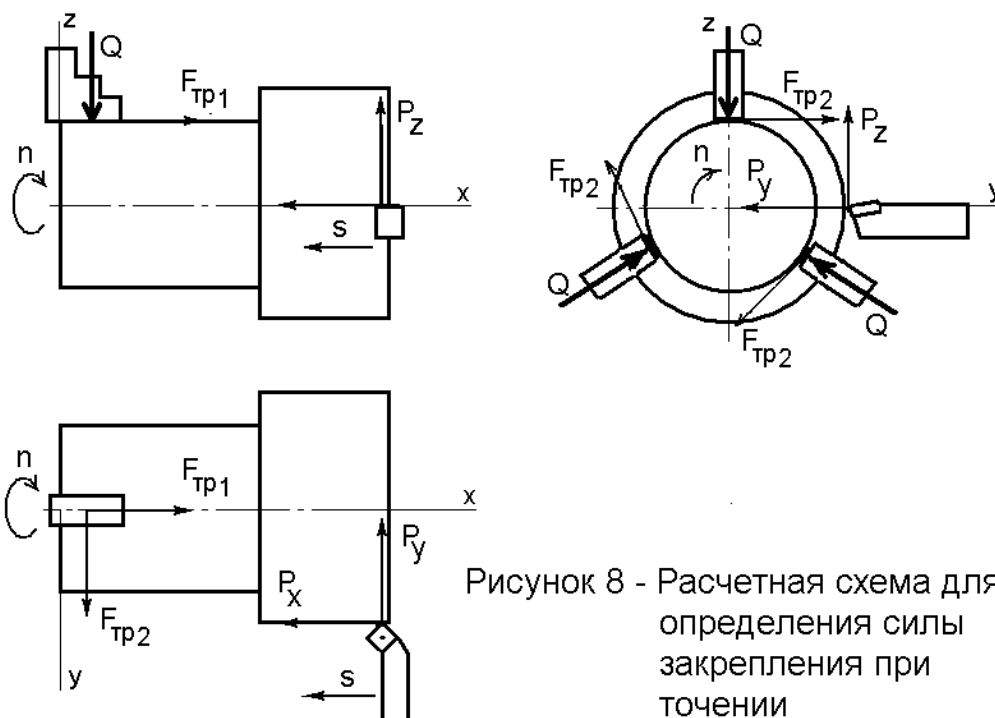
Расчетная схема для определения силы закрепления при точении
